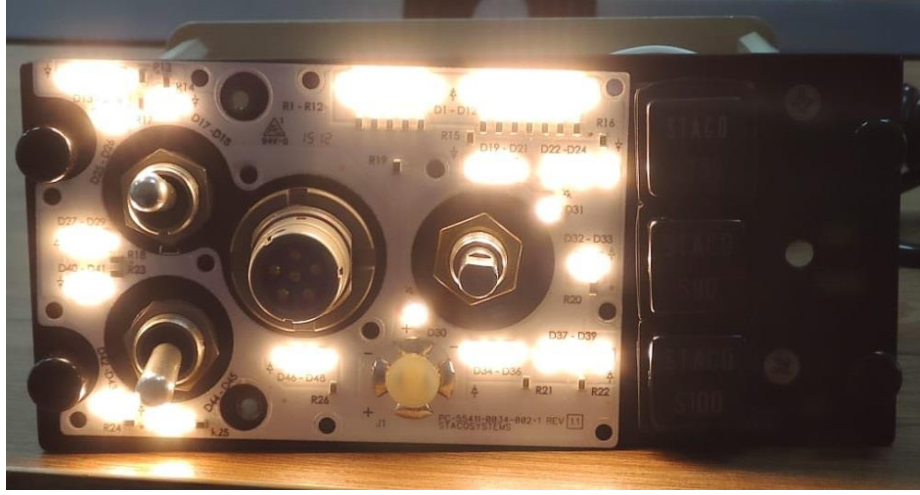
Devre Kartı (PCB) – SMD LED'ler (sarı ile)
